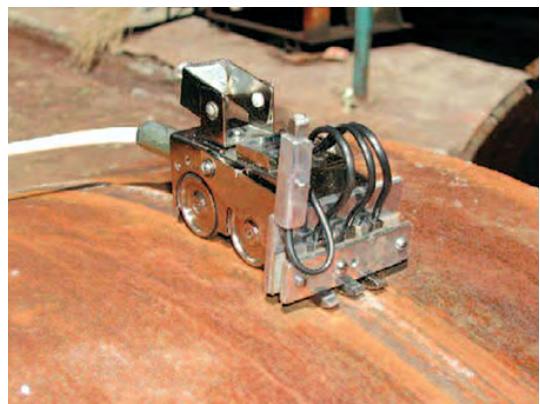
Inspección de defectos en una soldadura de tubería ferromagnética usando métodos magnéticos.²
